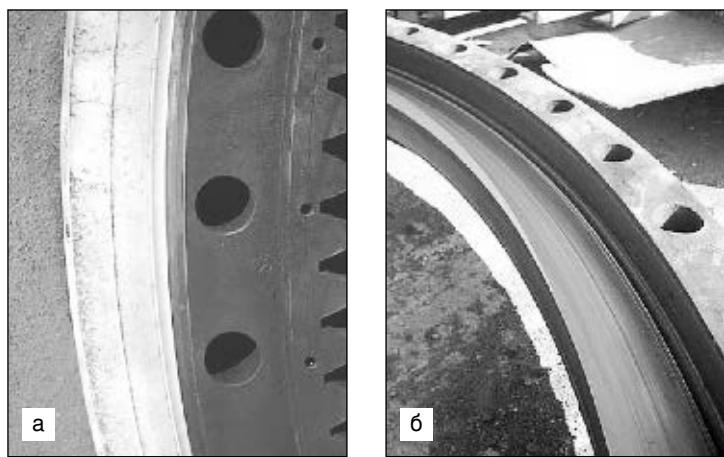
Внешний вид изношенных поверхностей катания зубчатого (а) и соединительного (б) колец ОПУ
